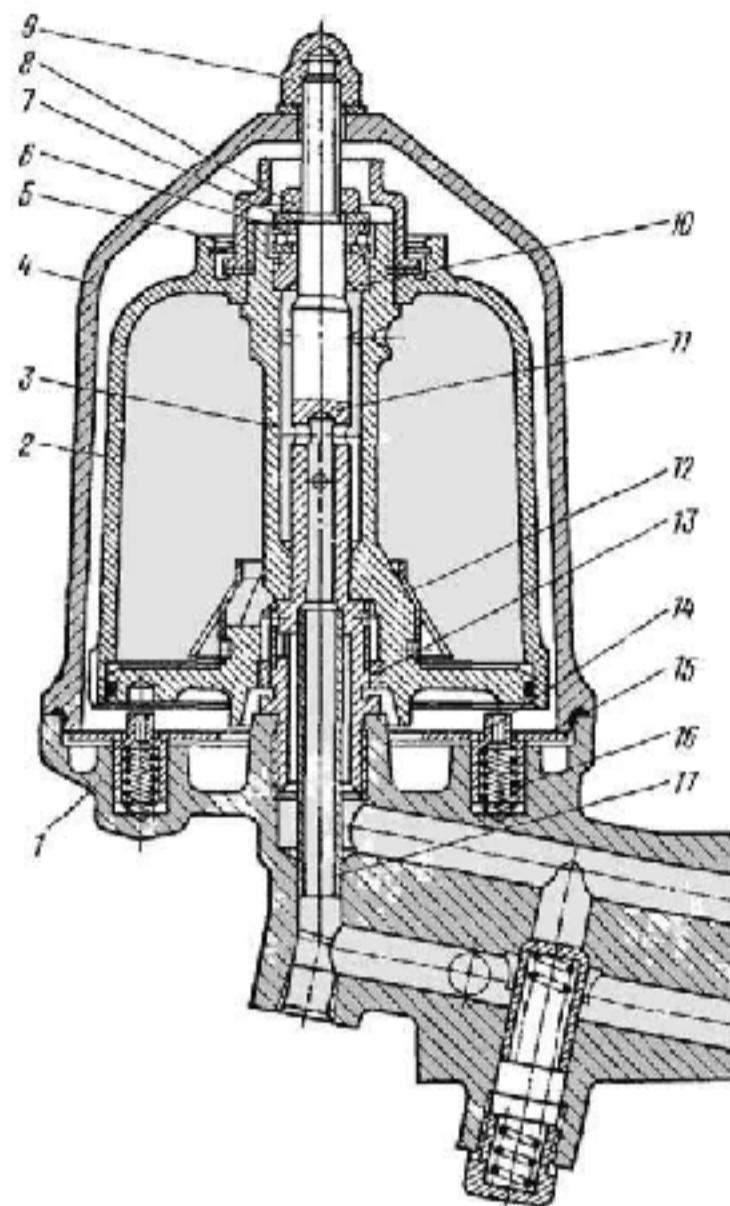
Центробежный масляный фильтр 1- корпус,2- колпак ротора,3- ротор,4- колпак фильтра,5- гайка крепления колпака ротора,6- упорный шарикоподшипник,7- упорная шайба,8- гайка крепления ротора,9- гайка крепления колпака фильтра,10- верхняя втулка ротора,11- ось ротора,12- экран,13- нижняя втулка ротора,14- палец стопора,15- пластина стопора,16- пружина стопора,17- трубка отвода масла
